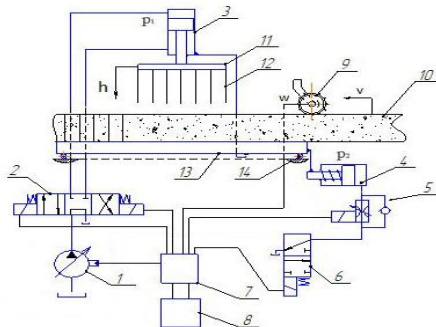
Гідравлічна схема автоматизованого пристрою для формування заготовок цегли
